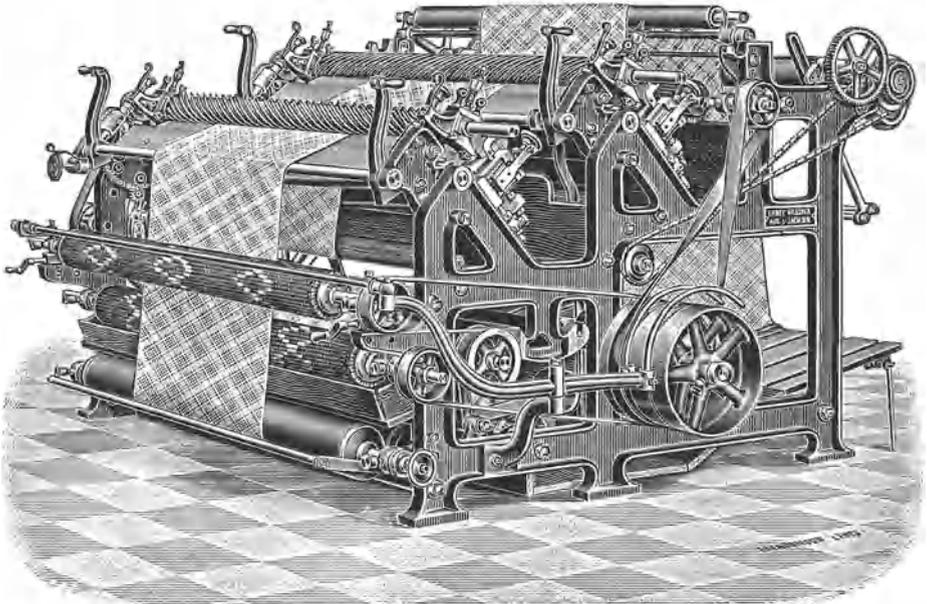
Schermaschine mit zwei Scherzylindern von Geßner.
